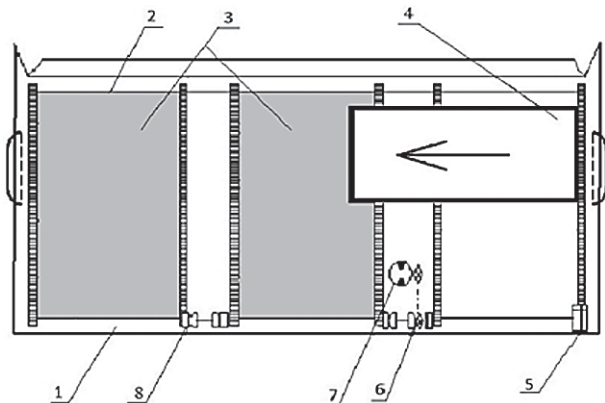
Схема транспортёра порционной жатки с устройством для образования стерневых кулис: 1 – ведущий вал; 2 – ведомый вал; 3 – транспортёрная лента; 4 – наклонный лоток; 5 – механизм натяжения; 6 – цепная передача; 7 – гидромотор привода транспортёра; 8 – карданный вал
